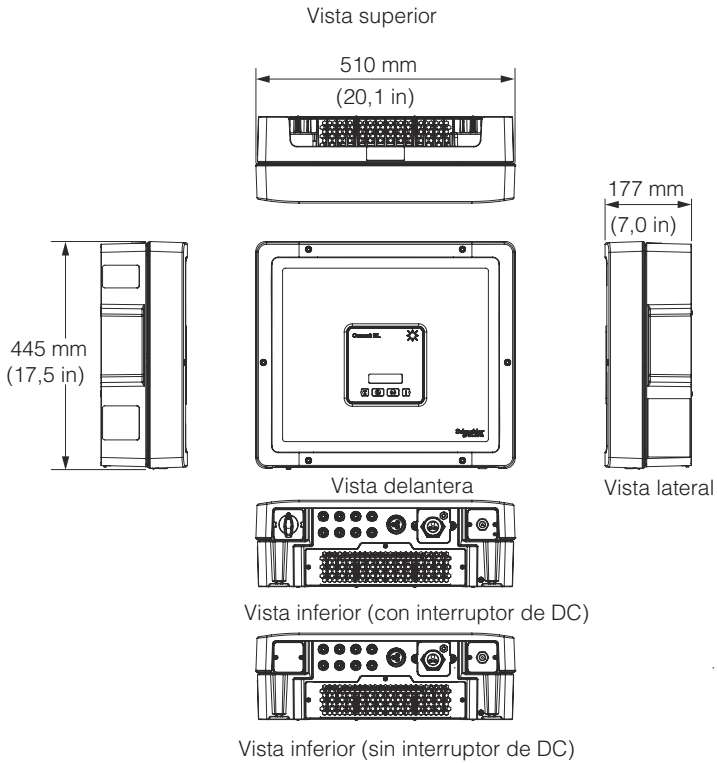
Vistas y dimensiones de Conext RL 5000 E-S/5000 E
